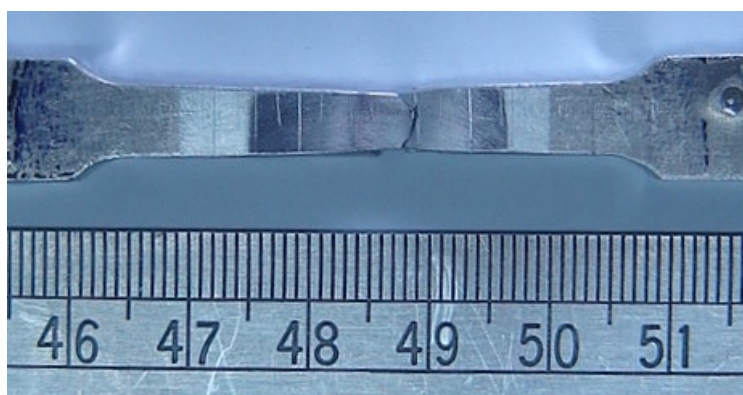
Ruptura sobre o cordão de solda FSW - geometria facetada.
